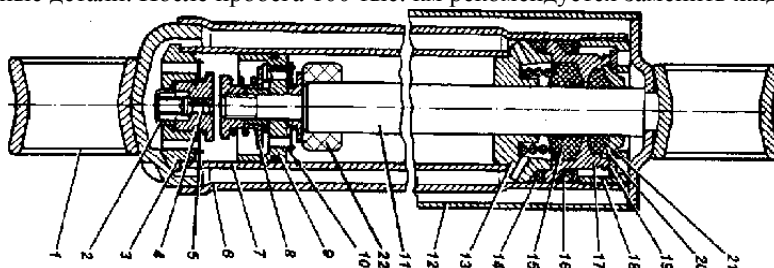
Амортизатор: 1 -проушина; 2 -ограничитель клапана сжатия; 3 -корпус клапана сжатия; 4 -клапан сжатия; 5 - впускной клапан; 6 -резервуар; 7 -цилиндр; 8 -клапан отдачи; 9 -поршень; 10 -перепускной клапан; 11 -шток; 12 -кожух; 13 -направляющая втулка штока; 14 -нижнее уплотнительное кольцо; 15 -сальник; 1" -верхнее уплотнительное кольцо; 17 -обойма сальников; 18 -гайка резервуара; 19 -шайба, 20 -защитное кольцо; 21 -сальник штока; 22 -буфер отбоя (только для передних амортизаторов)
